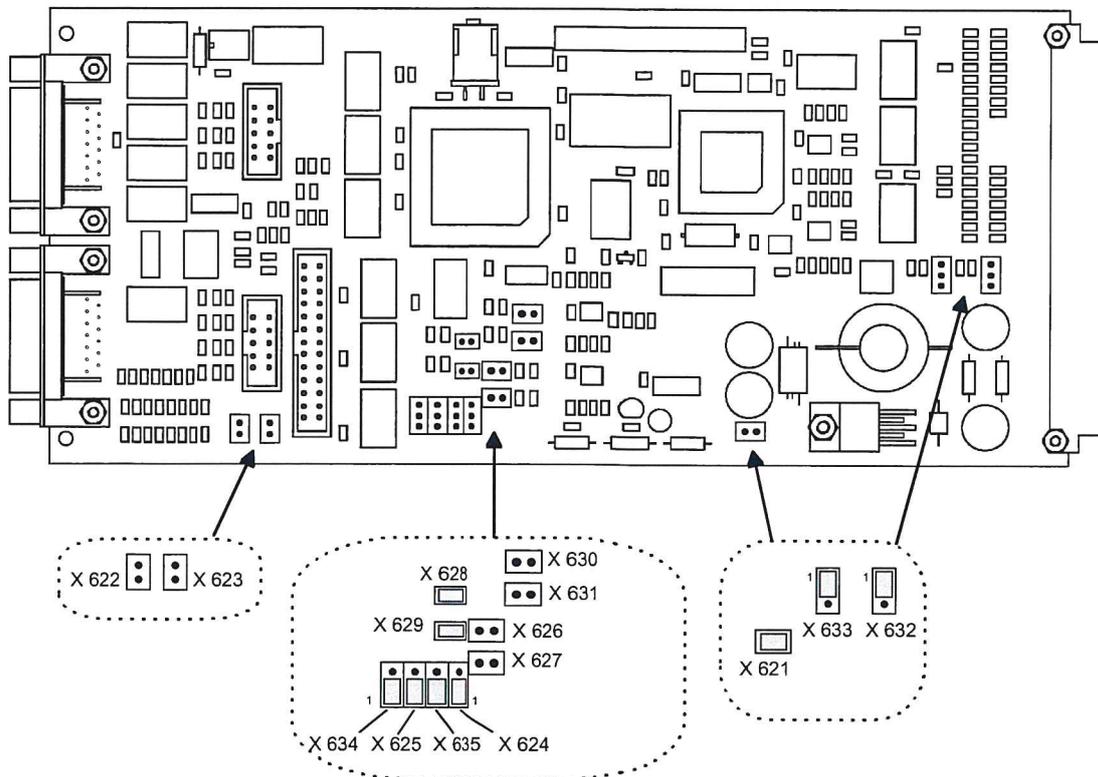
16: Kodierelemente auf dem Steuerprozessor
